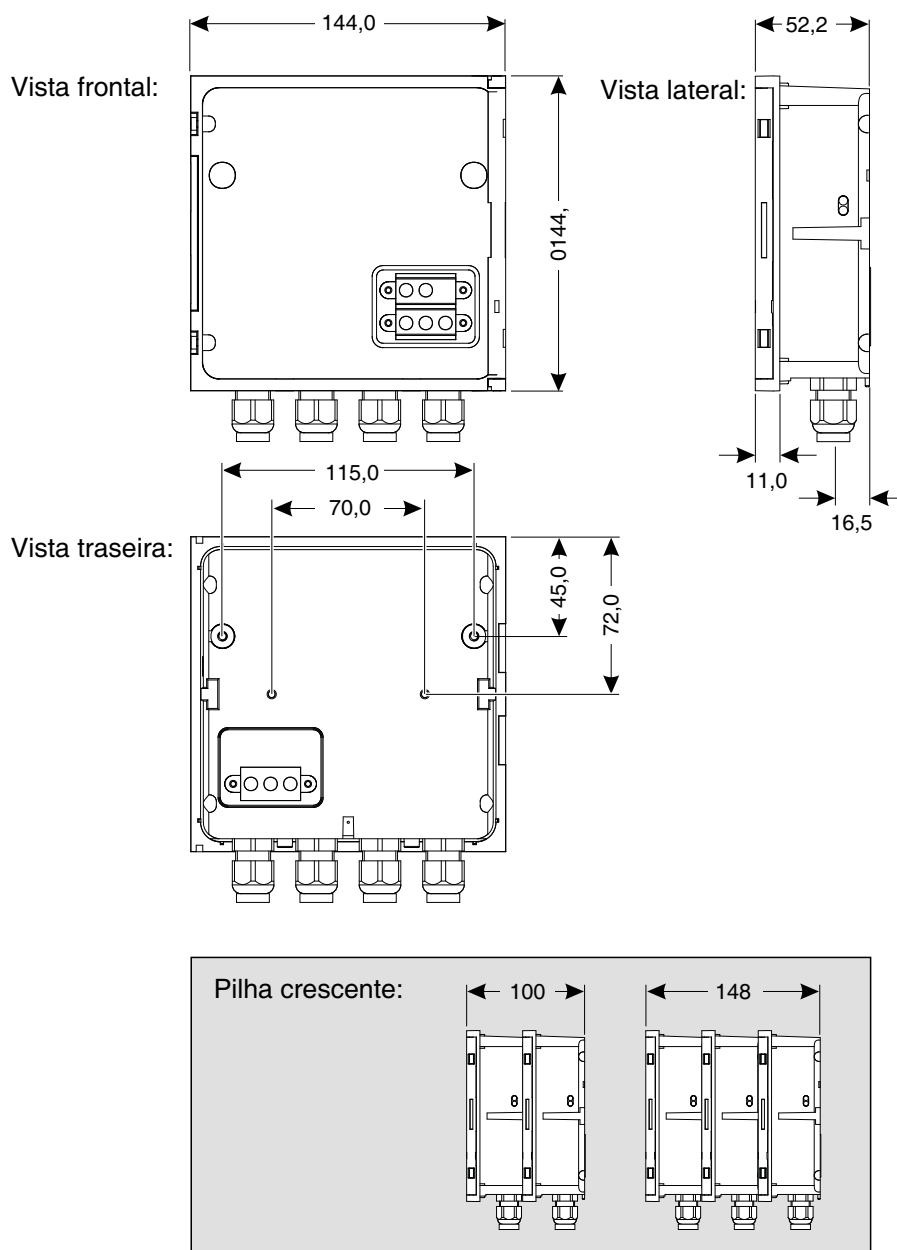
Esboço das dimensões do módulo MIQ^o (dimensões em mm)
